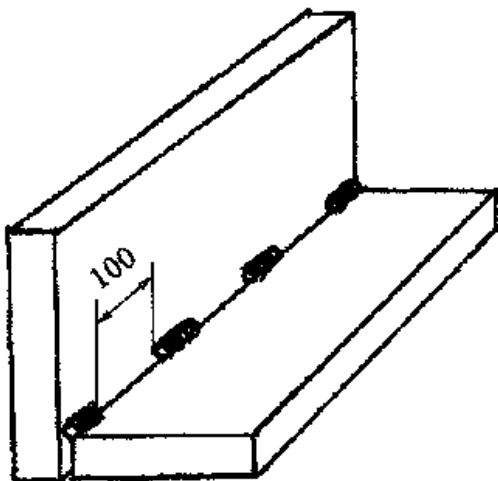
Технология сборки сварных соединений с помощью шаблонов
